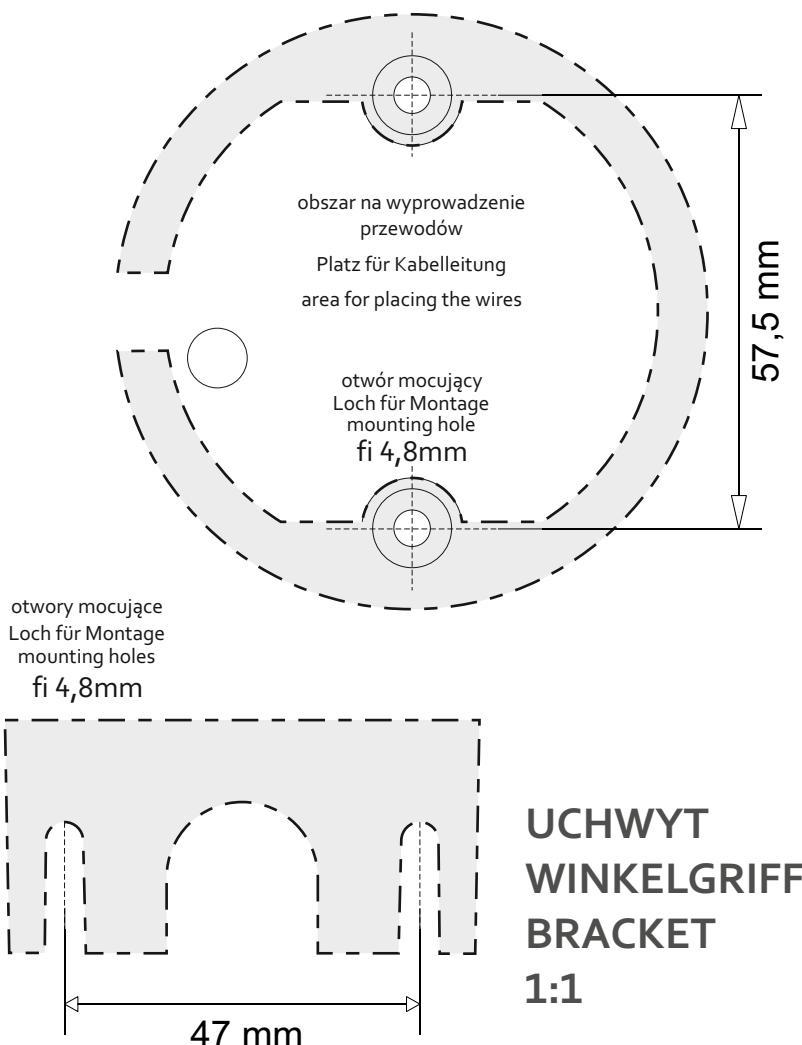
Montaż lampy do powierzchni pionowej za pośrednictwem uchwytu kątowego.
